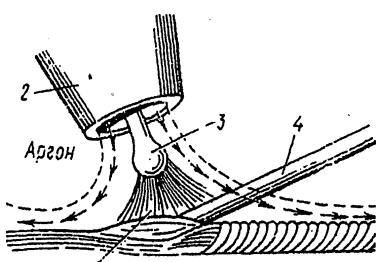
Дуговая сварка в защитных газах неплавящимся электродом:
